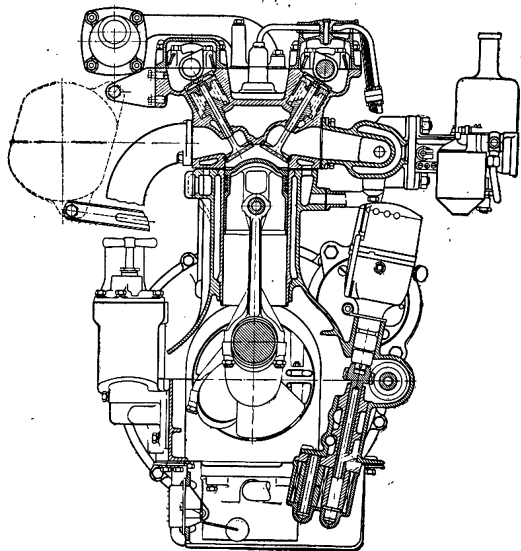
Поперечный разрез двигателя автомобиля «Эйстон-Мартин»
